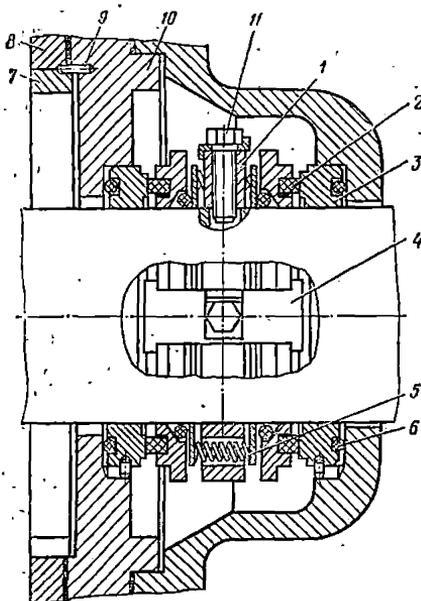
Сальник компрессора П110: 1 — обойма; 2 — кольцо графитовое; 3 — кольцо стальное; 4 — планка; 5 — пружина; 6 — кольцо уплотнительное резиновое; 7 — стакан подшипника; 8 — блок картера; 9 — штифт; 10 — диск сальника; 11 — винт
